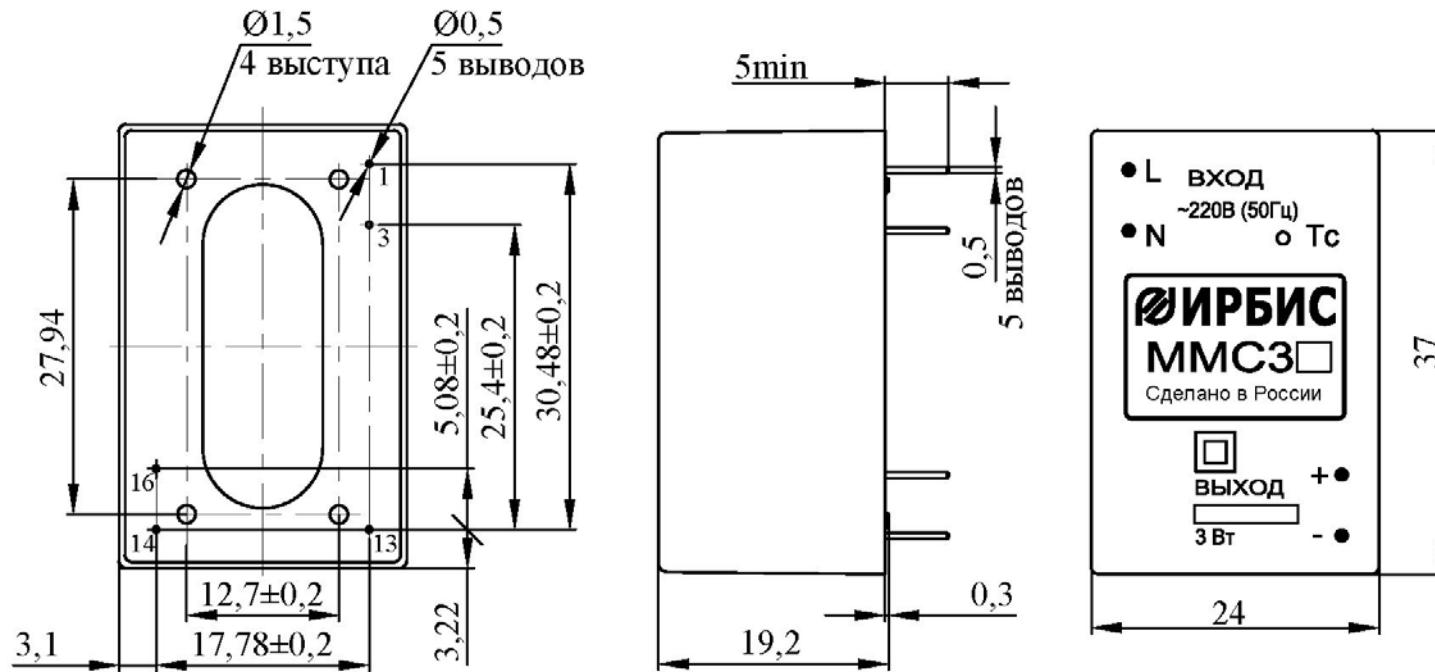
Габаритный чертеж модулей серии MMC3
